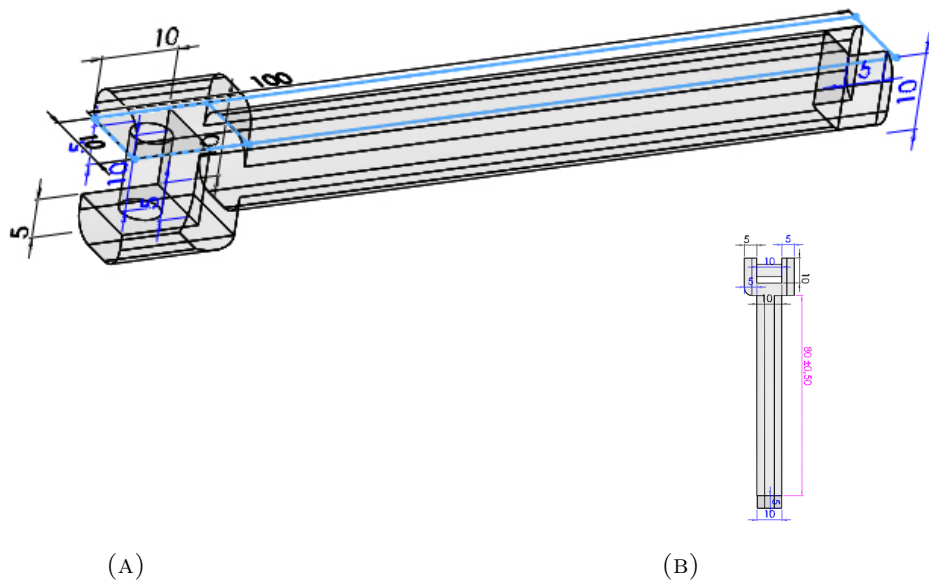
Segment 3 : la figure (3.9a) montre une vue en 3-D. La figure (3.9b) montre la vue de face et décrit les mesures et les dimensions du segment.
